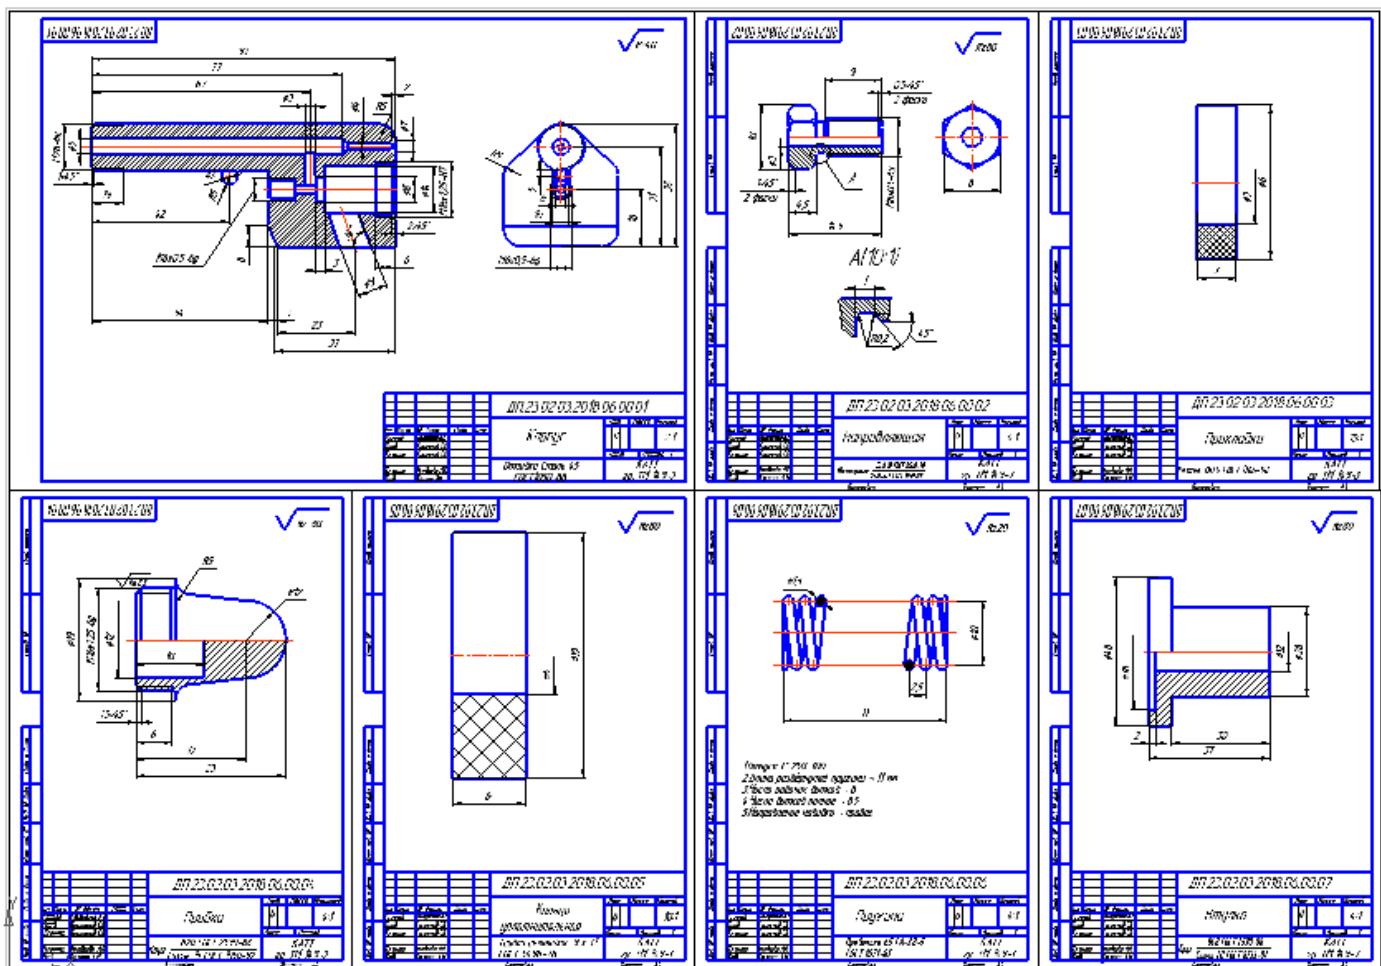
Примеры выполнения рабочих чертежей деталей
